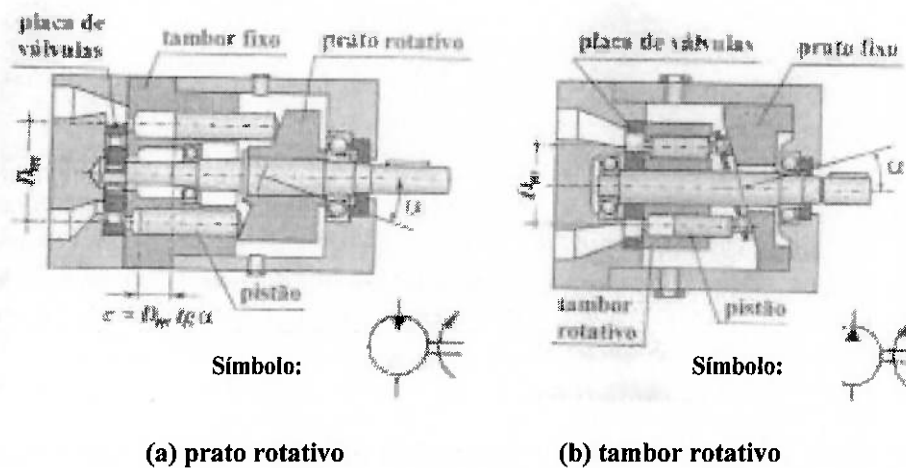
Tipos de máquinas de prato inclinado. (a) motor fixo e símbolo; (b) bomba fixa e símbolo
